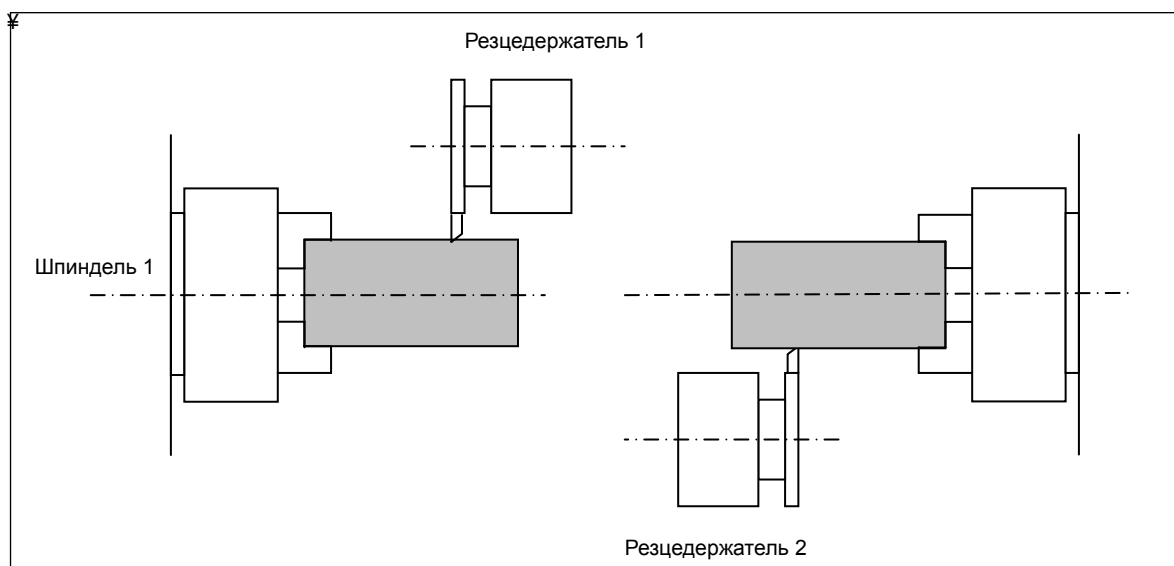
(b) Пример использования на токарном станке с двумя шпинделями и двумя резцедержателями
